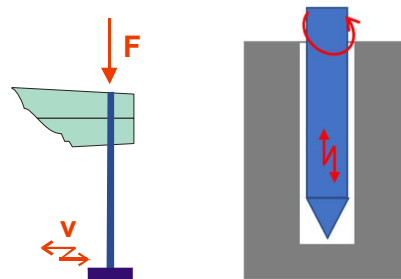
Reibkontakt beim Metallschweißen mit Ultraschall (links) und beim Bohren (rechts).
